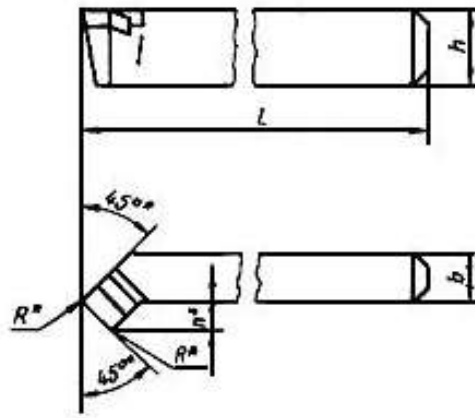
Резец токарный проходной отогнутый с пластиной из твердого сплава ГОСТ 18877-73
